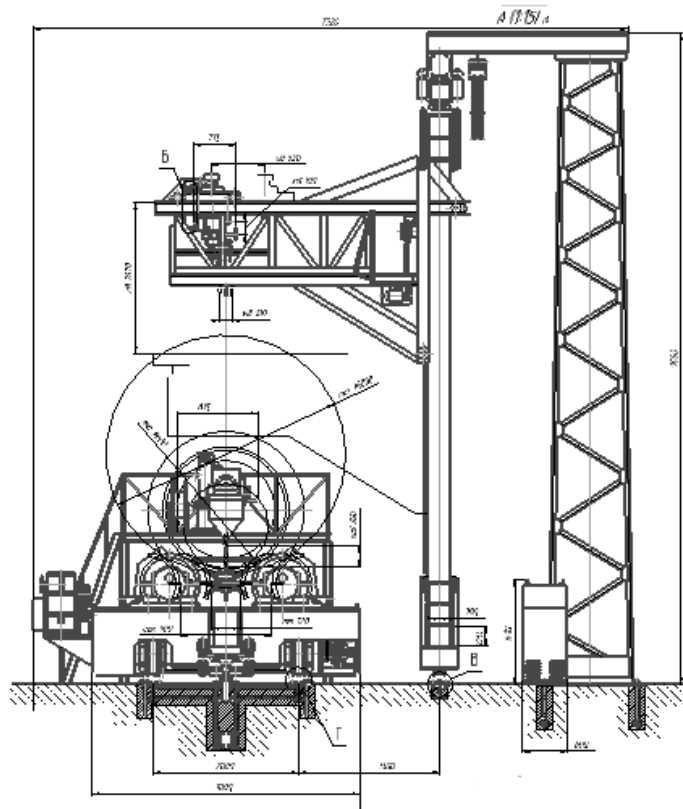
Стенд для складання та зварювання автоклаву
